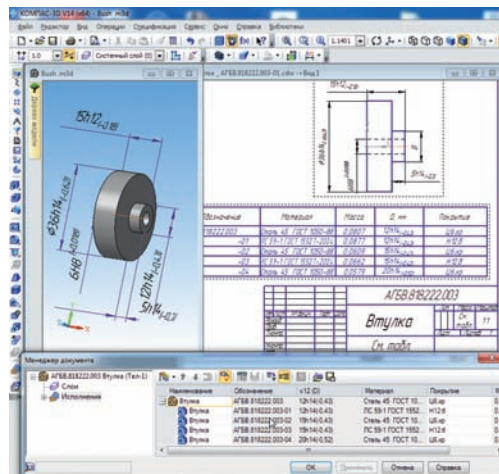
Модель и ассоциативный чертёж детали с исполнениями
